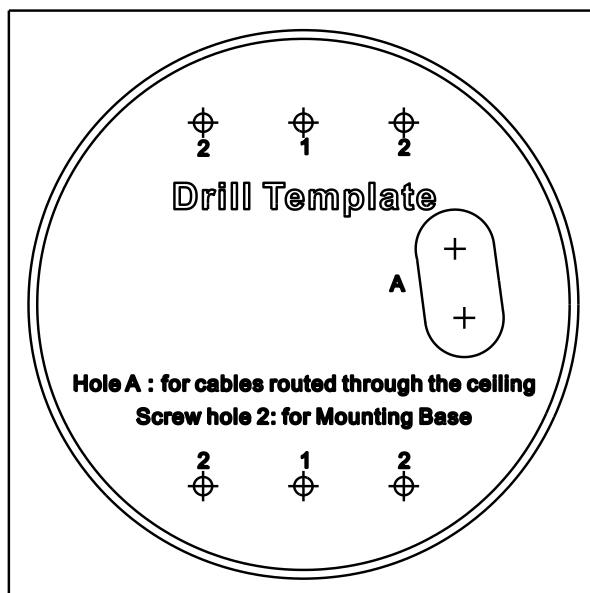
Шаблон для разметки крепежных отверстий. Монтаж на поверхность
